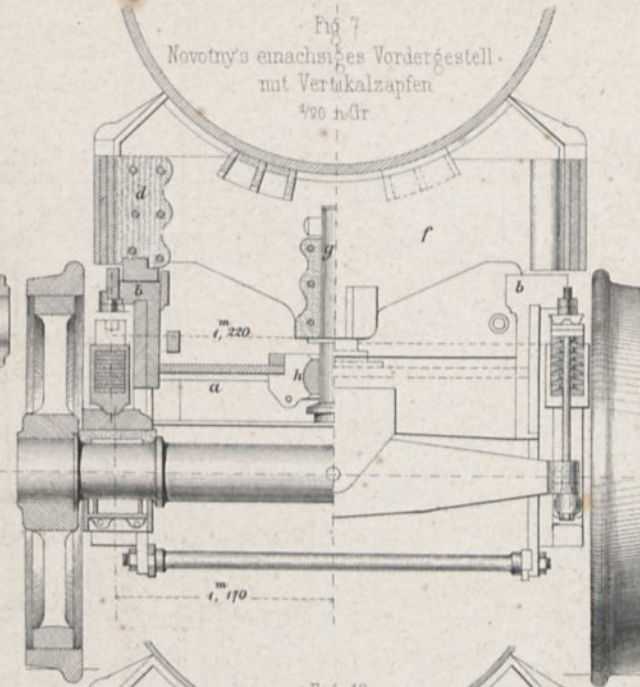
Novotny's einachsiges Vordergestell mit Vertikalzapfen 1/20 n.Gr.
